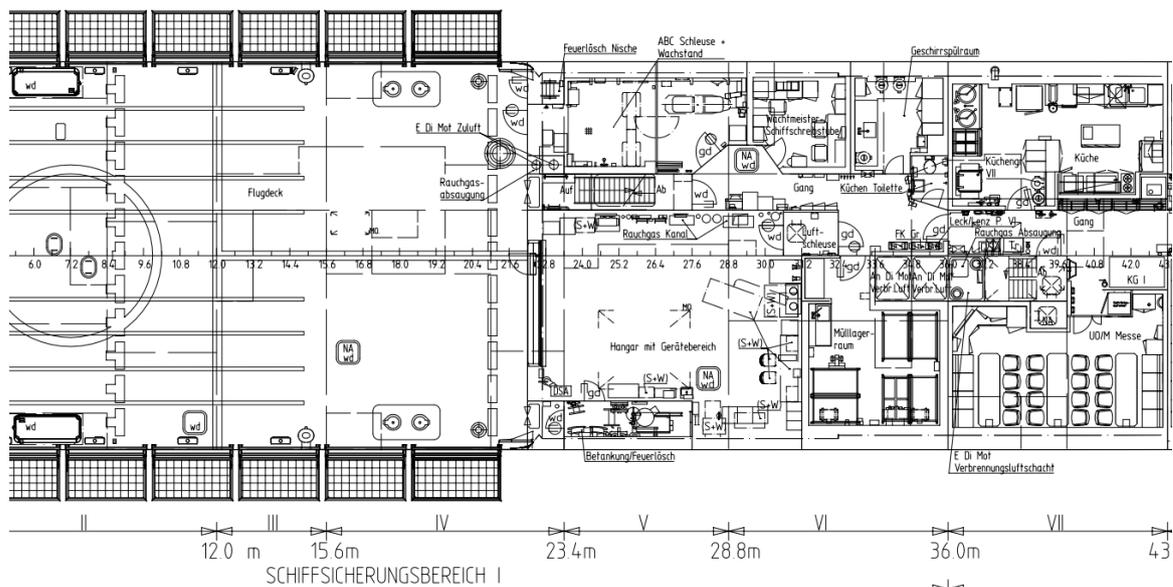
Ausschnitt Generalplan K 130 Los 2, Hauptdeck
